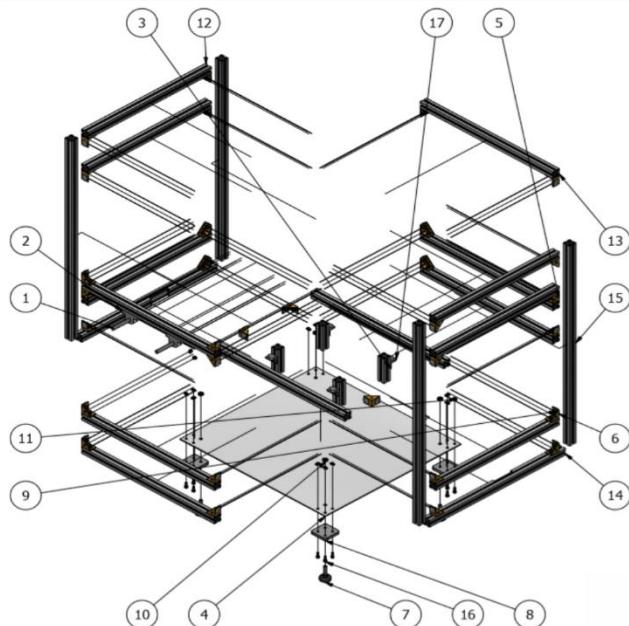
Acabamento Frontal, com indicações de cada componente.
